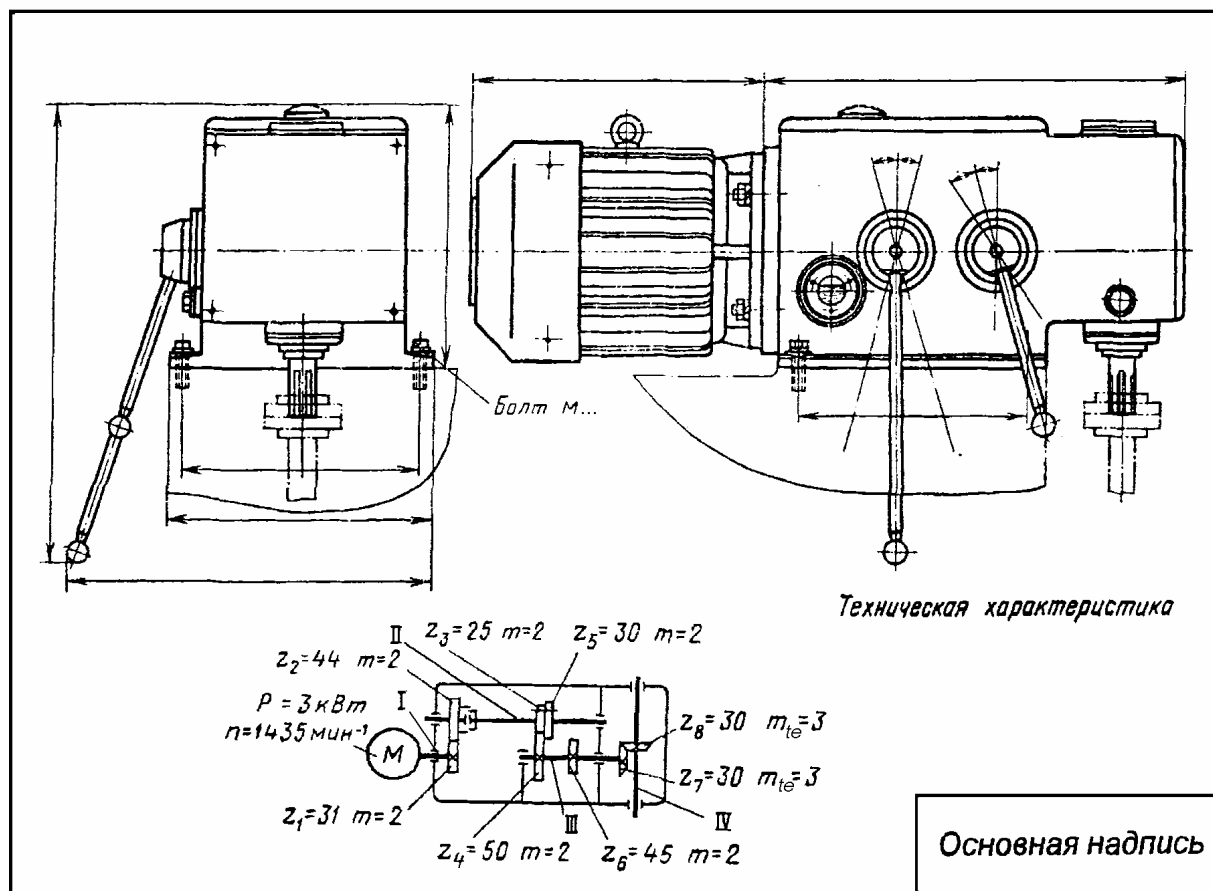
Общий вид привода сверлильного станка с установкой на станине
